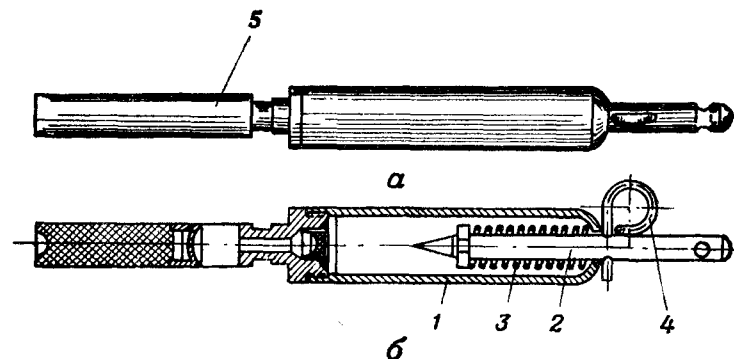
Модернизированный упрощенный взрыватель (МУВ):
